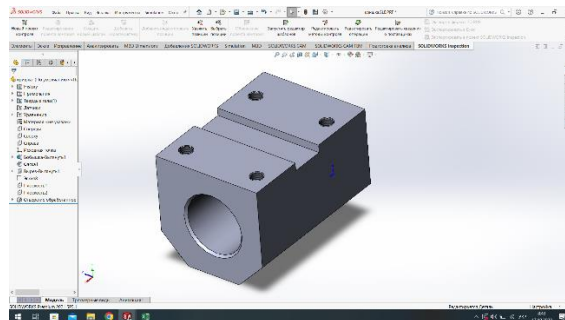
3D модель деталі корпус в програмі Solid Works
